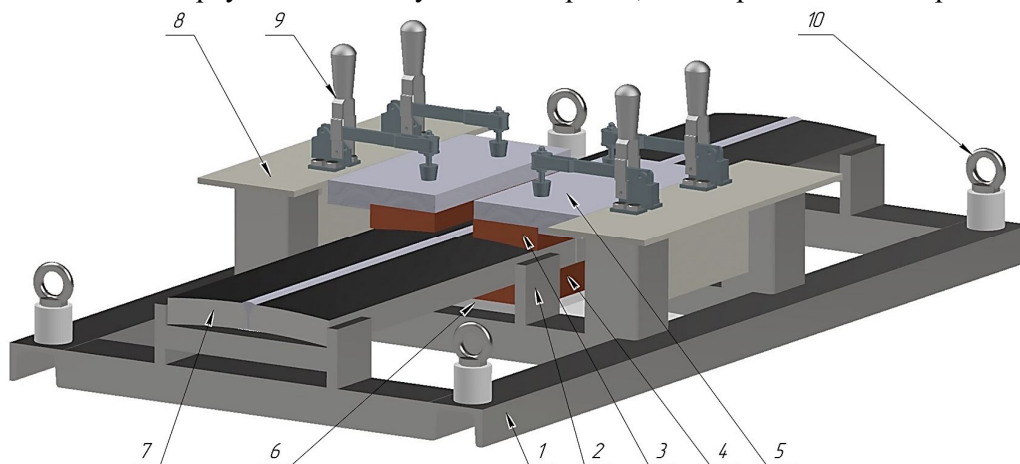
3D-модель приспособления. 1 – рамное основание приспособления; 2 – пластик; 3 – сменные медные прижимные планки; 4 – медная водоохлаждаемая подкладка; 5 – верхний стальной охладитель; 6 – стальное основание; 7 – образец; 8 – плита крепления сварочных прижимов; 9 – прижим сварочный; 10 – рым-болты.
